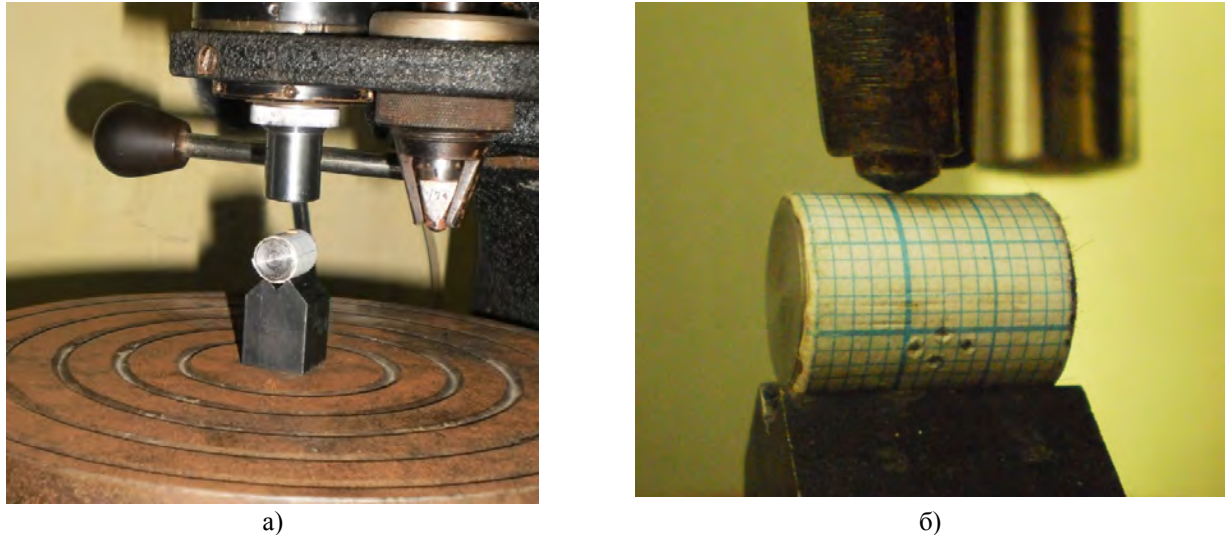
Нанесение сетки на боковую поверхность цилиндрического образца: а) установка образца на рабочий стол твердомера; б) вдавливание индентора в материал образца
